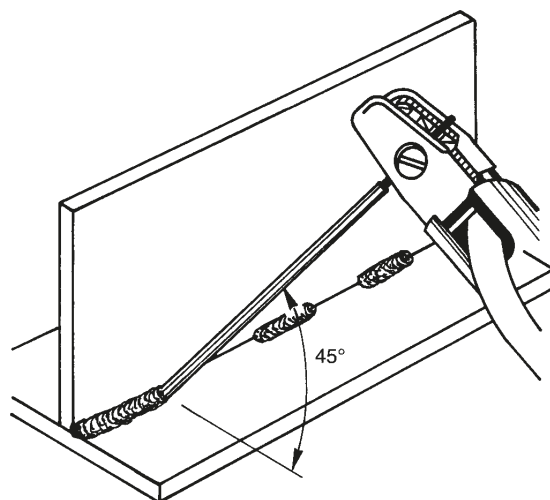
Schweißen in der Horizontal-Vertikalposition
